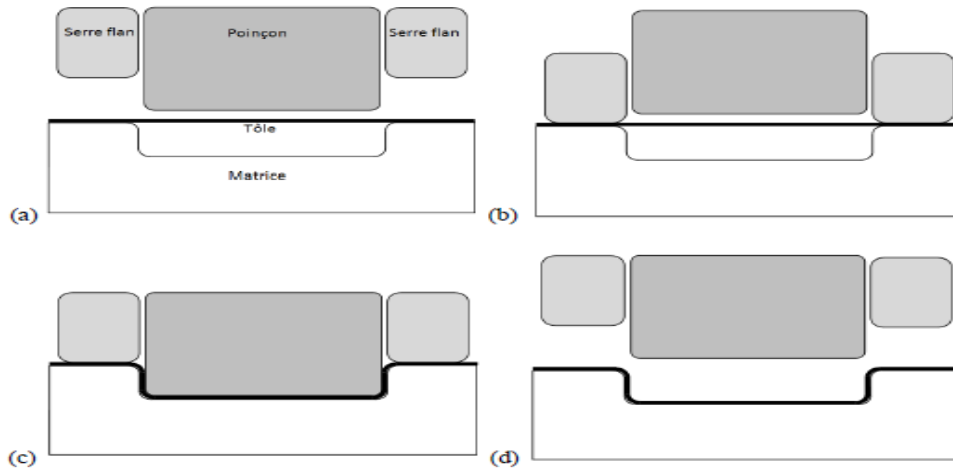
Principales étapes d'une opération d'emboutissage. (a) Positionnement du flan, (b) serrage, (c) descente du poinçon et (d) remontée des outils mobiles. [30].
